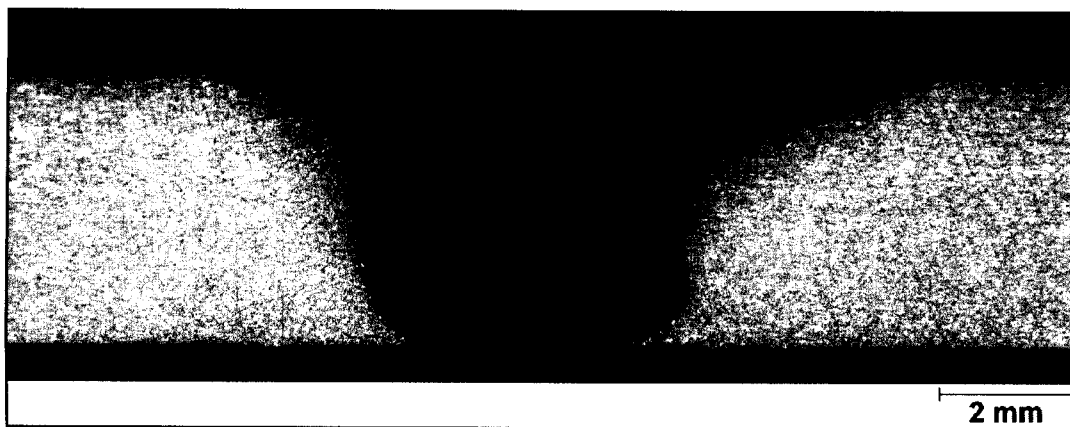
Macrografia de uma secção transversal das chapas soldadas com 650 rpm e 250 mm/min. Ataque: reagente Keller.
